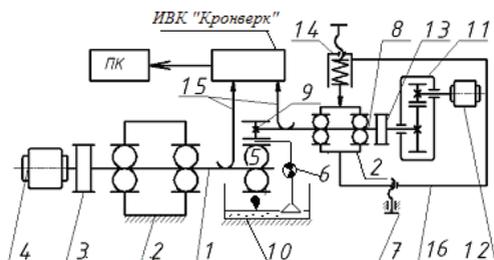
Кинематическая схема стэнда для обработки подшипников качения:
